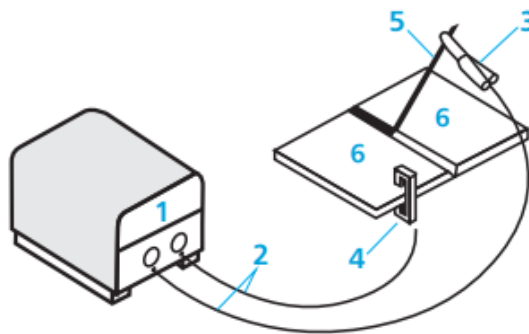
Elementos de soldadura por arco eléctrico
